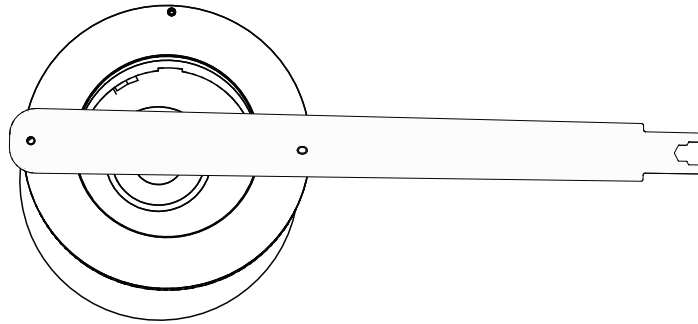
Entfernen der Endabdeckung mit dem Mehrzweck-Werkzeug
